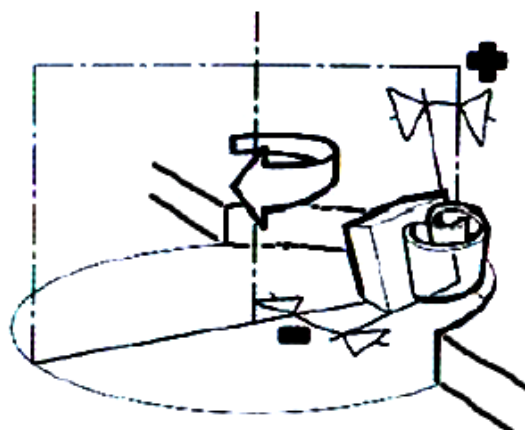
Dvojitá pozitivní geometrie [2].
